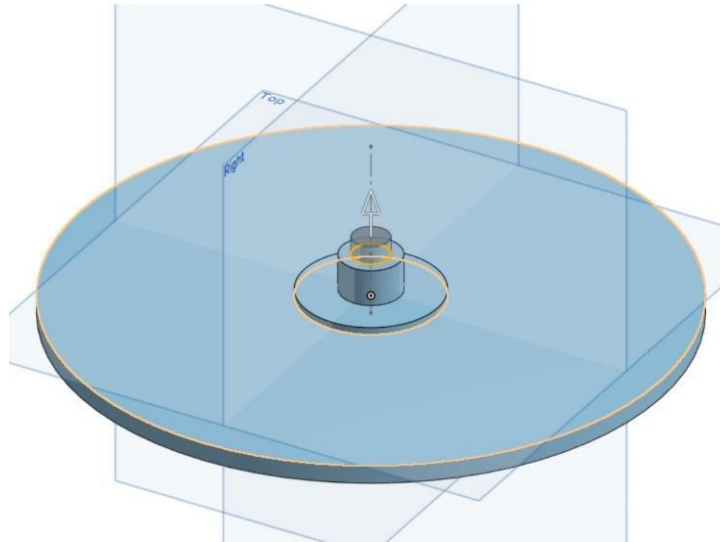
Вигляд основи нижньої частини з валом для підшипника
